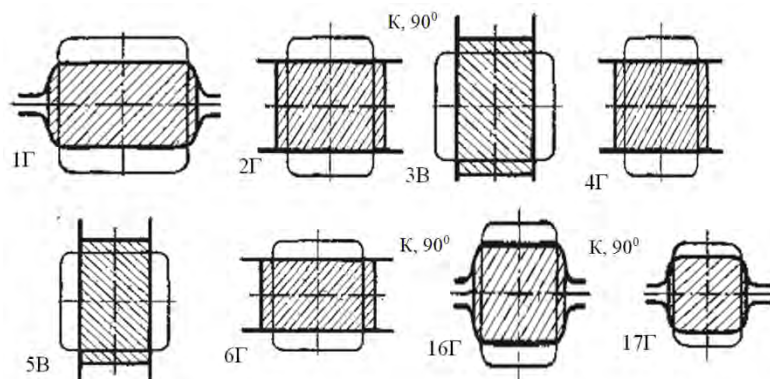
Предлагаемая для крупносортного стана 600 система ящичный калибр – гладкая бочка
